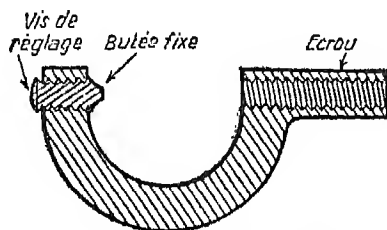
Ecrrou d'un palmer. Coupe de la pièce en forme de C. Remarquez à gauche, la vis de réglage qui se termine par la butée fixe. La surface extérieure de l'écrou porte une graduation en millimètres.
